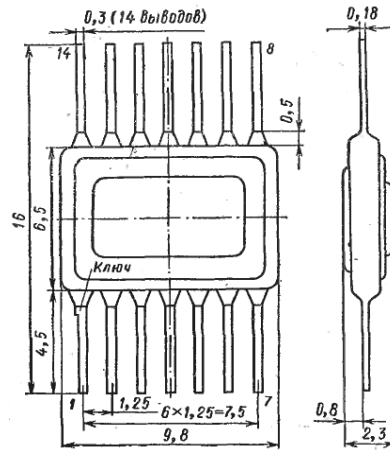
Корпус мікросхеми К249ЛП1А
